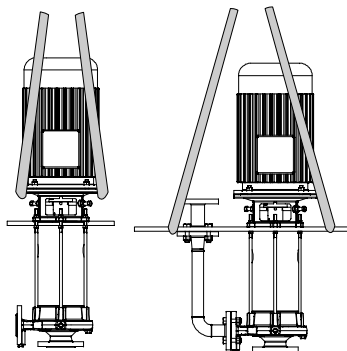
Транспортировать насосный агрегат с крышкой/без крышки до размера двигателя 160
